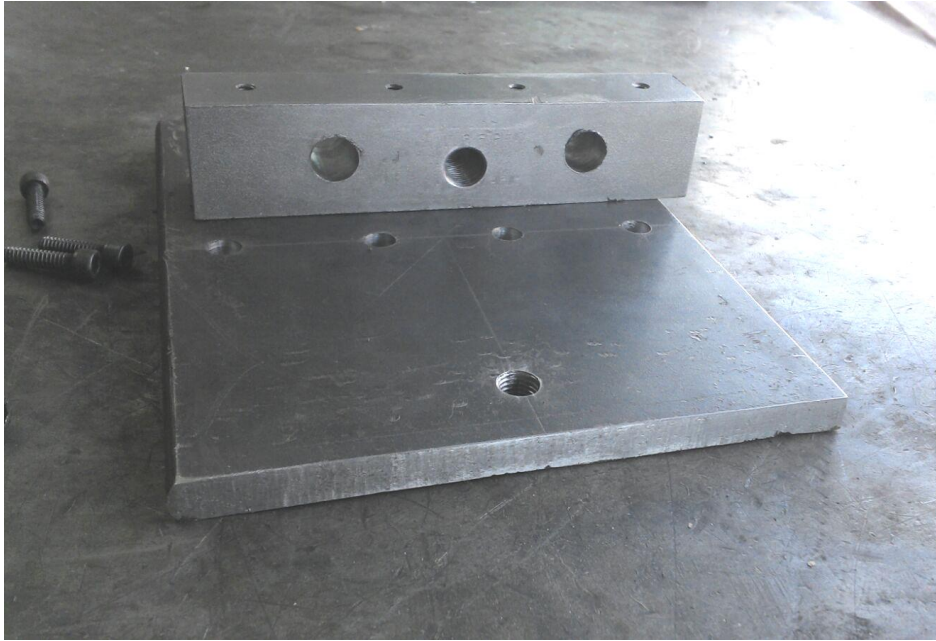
Base del conjunto motor-piedra. En esta se sujeta el conjunto motor-piedra.
